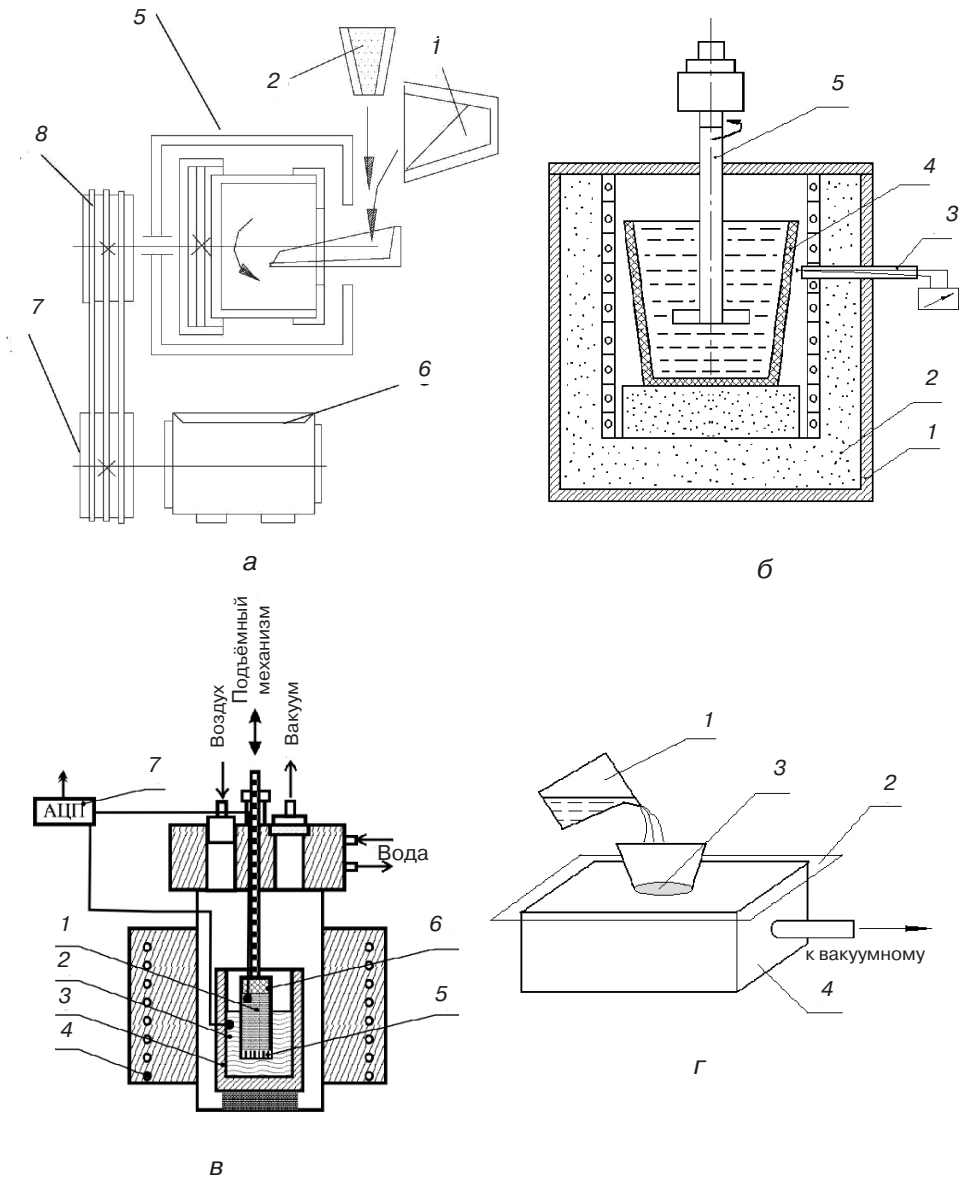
Некоторые схемы получения композиционных материалов литейными методами: а – ковш с расплавом алюминия (1), ковш с дисперсным наполнителем (2), кокиль (5), электродвигатель (6), большой шкив (7), меньший шкив (8); б – металлический кожух (1), огнеупорная футеровка (2), термопара (3), тигель (4), мешалка (5); в – порошковая смесь (1), металлический расплав (2), графитовый тигель (3), печь сопротивления (4), пористая заглушка (5), вакуумный буфер (6), аналогово-цифровой преобразователь (7); г – ковш с расплавом (1), полиэтиленовая плёнка (2), модель с зернистым наполнителем (3), ёмкость с песком (4)
